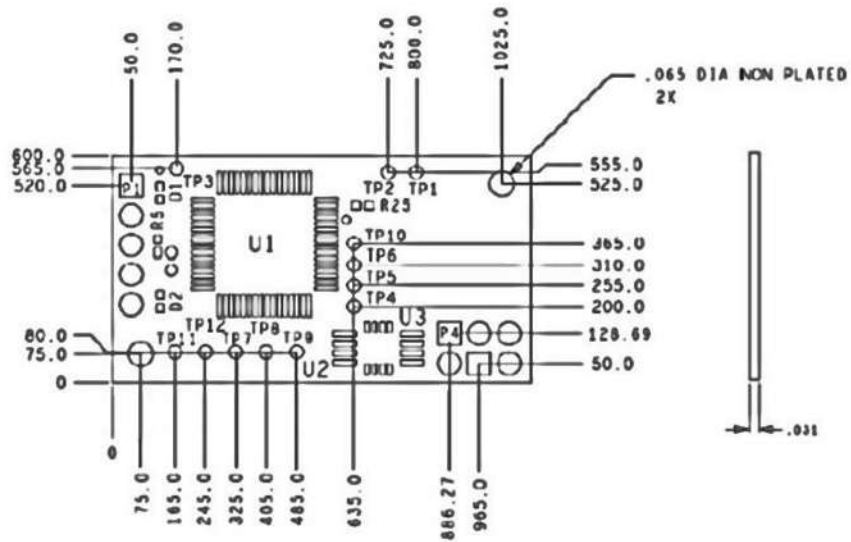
Dibujo mecánico de la placa del dispositivo ThinkGear de NeuroSky. [40]
